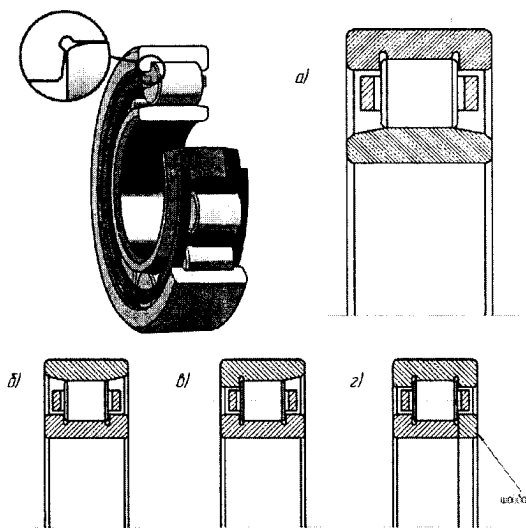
Роликовий радіальний однорядний підшипник з короткими циліндричними роликами
